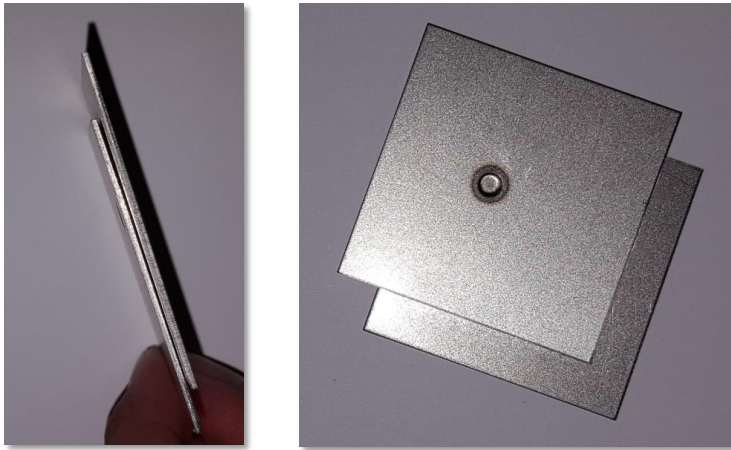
Zu Demonstrationszwecken mit dem System verschweißte Stahlbleche mit einer Dicke von jeweils 1mm.
